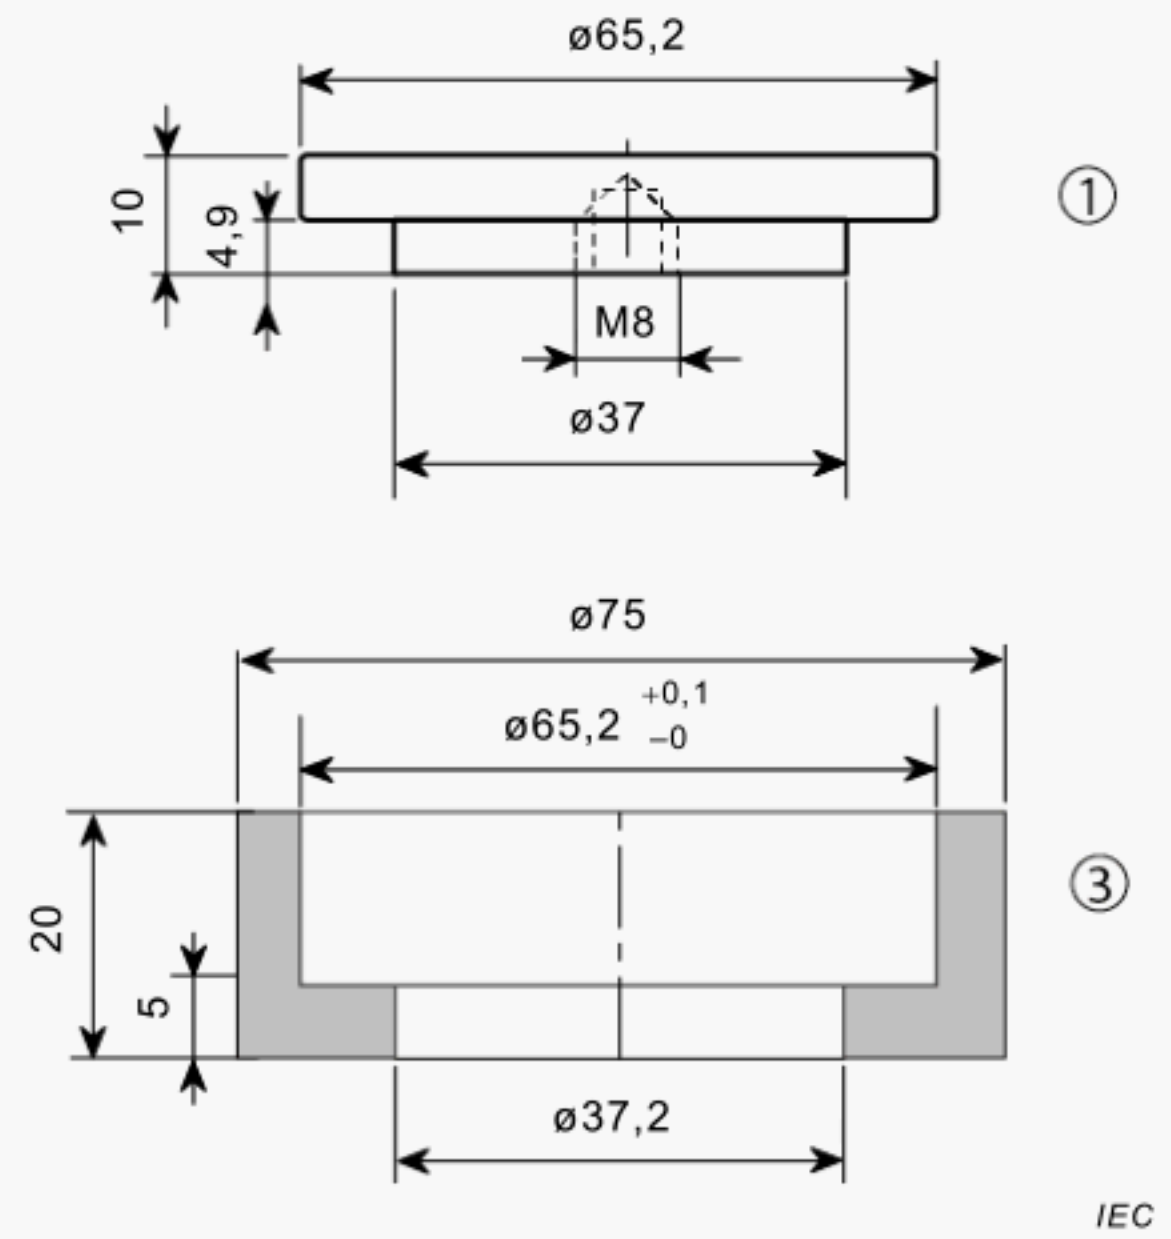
Pour tube rempli de mousse de 64 mm de diamètre
